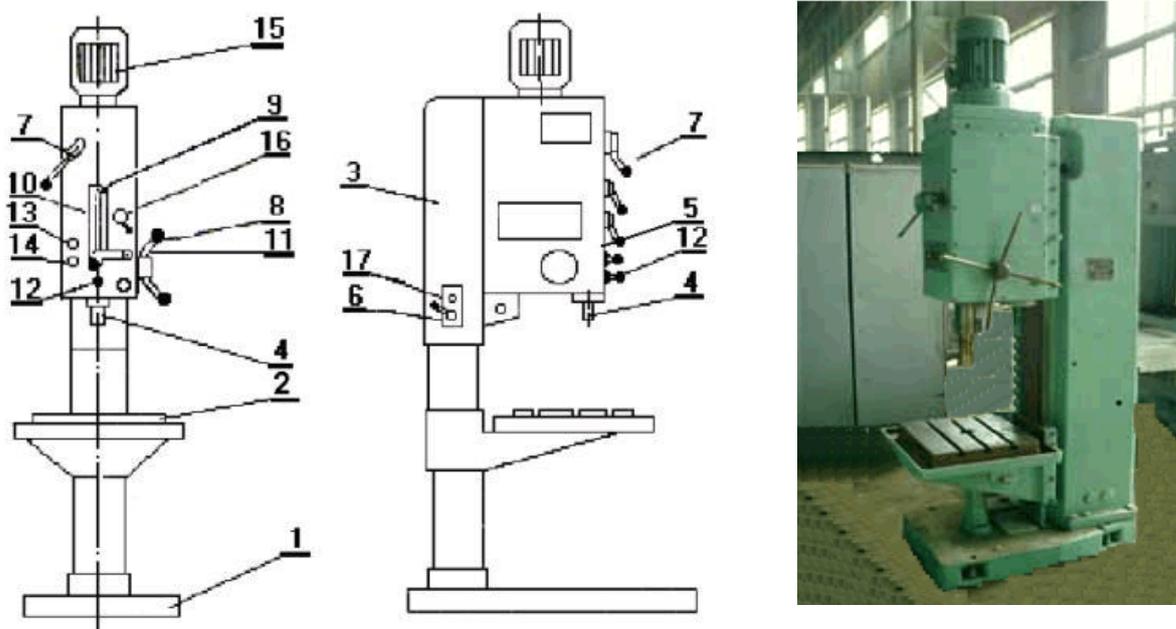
Схема и фотография вертикально-сверлильного станка:
